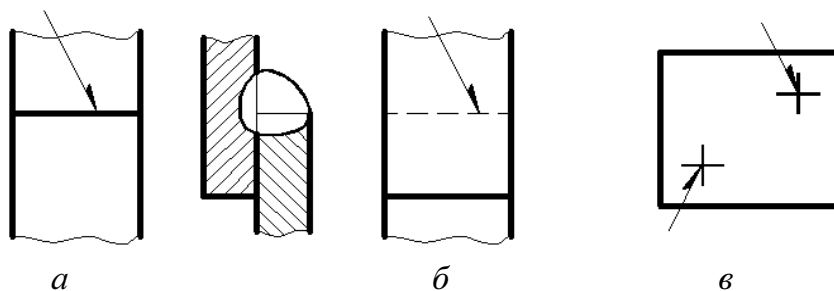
Изображение сварного шва и сварных точек:
